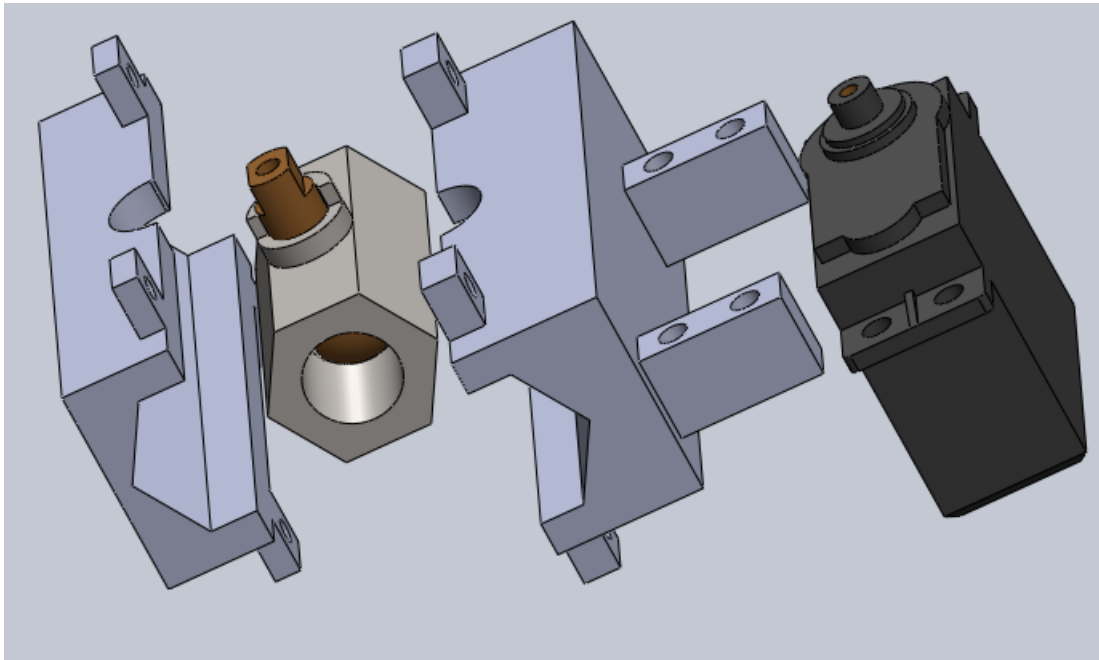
Válvula esférica adaptada com impressão em PLA com vista explodida.
